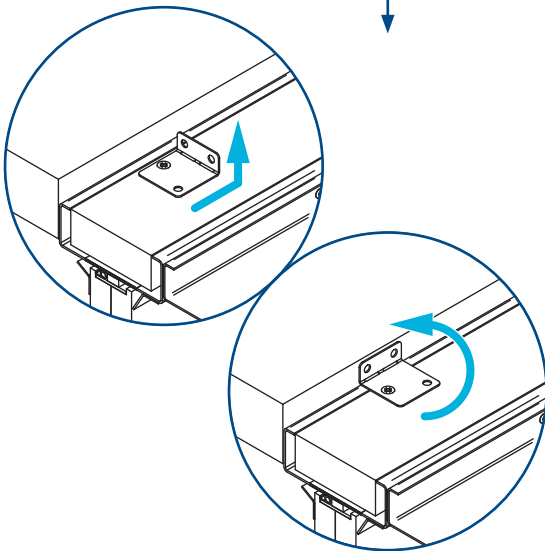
Biegen und Drehen des Fixierungswinkels bündig mit der Aufhängeebene
